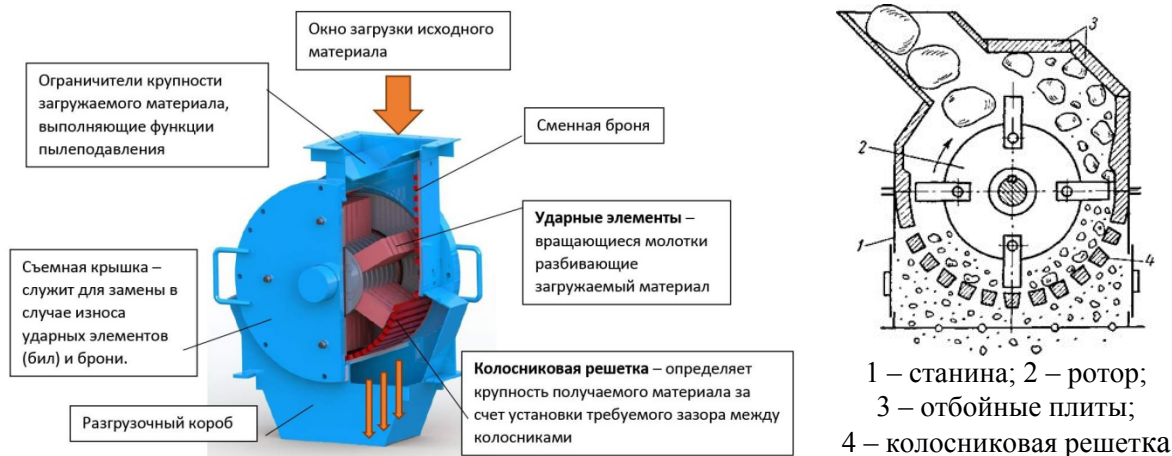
Механизм молотковой дробилки и конструктивная схема молотковой дробилки
